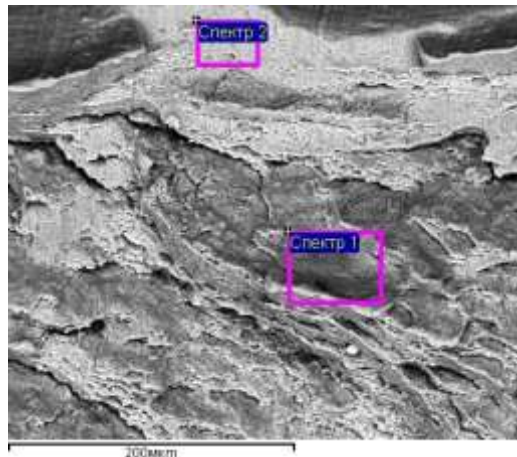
Излом приповерхностной зоны сварного соединения ДУАКМ 1565чМ + 20% Al₂O₃ с обезжириванием поверхности перед сваркой
